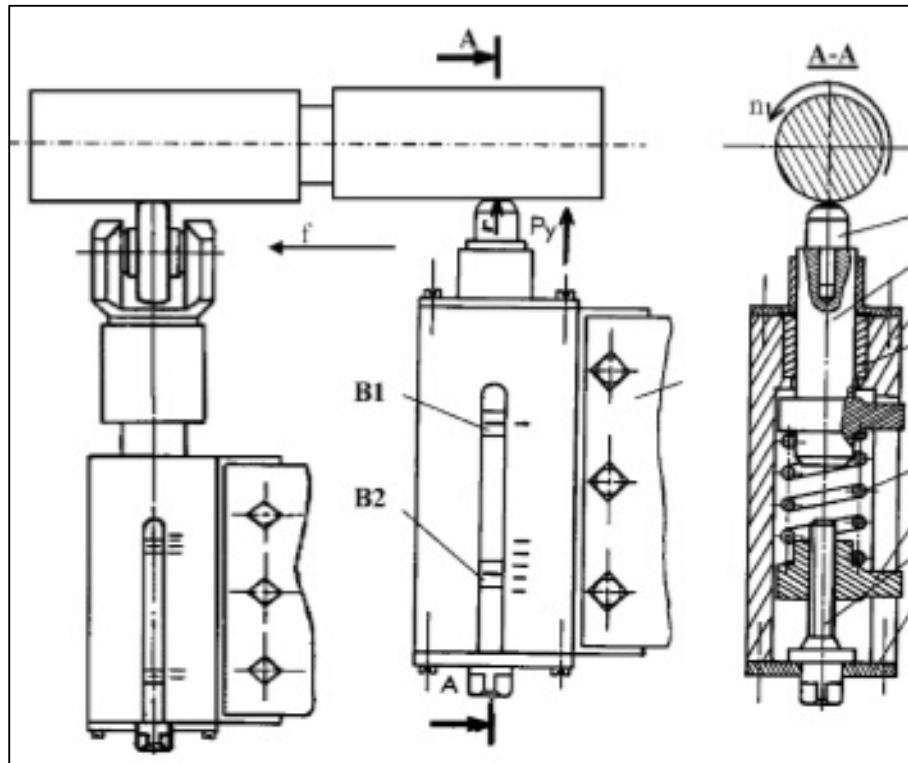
Equipamento de polimento com contato através de esfera ou rolete sobre superfície cilíndrica rotativa
